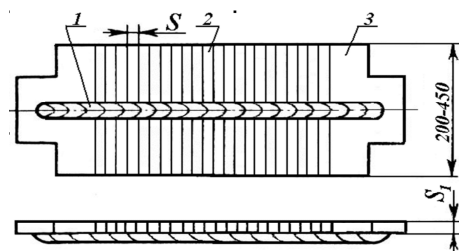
Пластина з наплавленням: 1 – валик; 2 – брусок; 3 – планка приставна.
